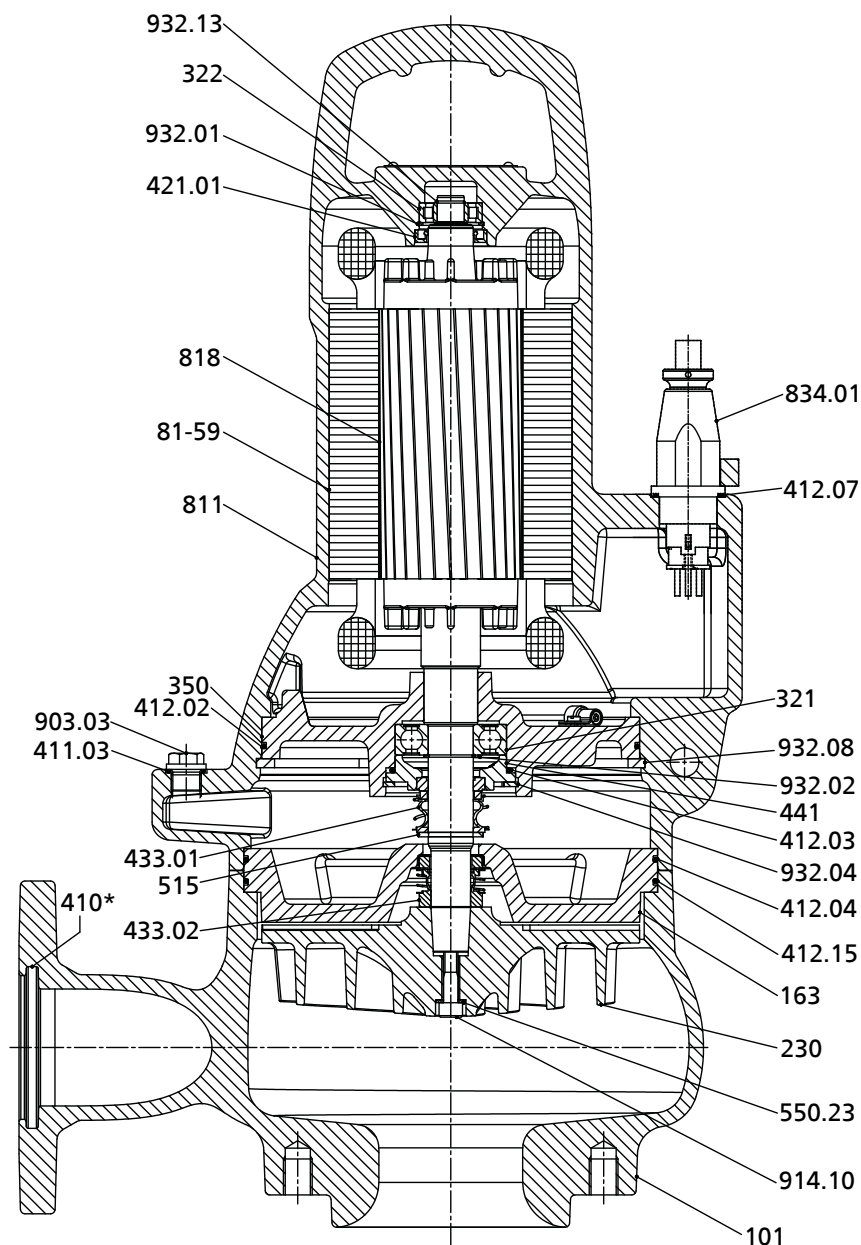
Сборочный чертеж Amarex KRT, тип двигателя 1
